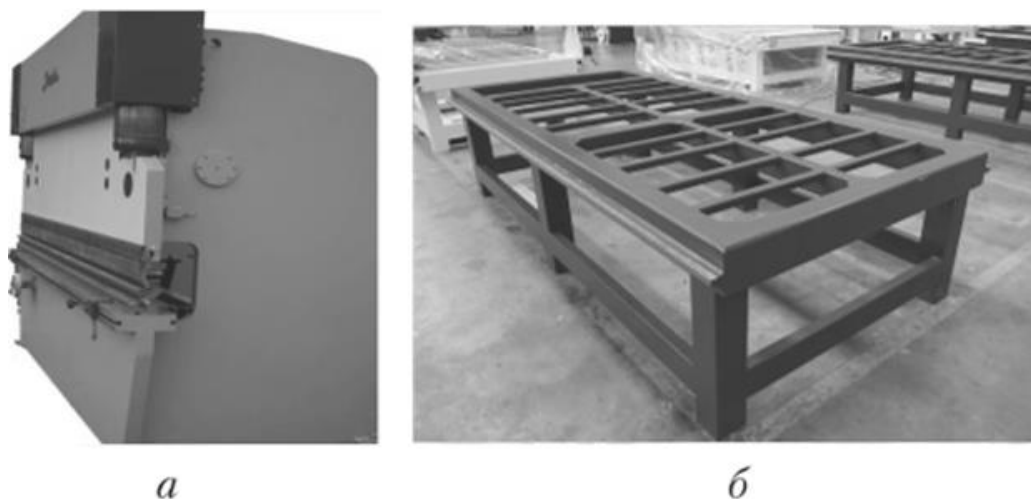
Зварені станини а) токарного і рами б) фрезерного верстата
